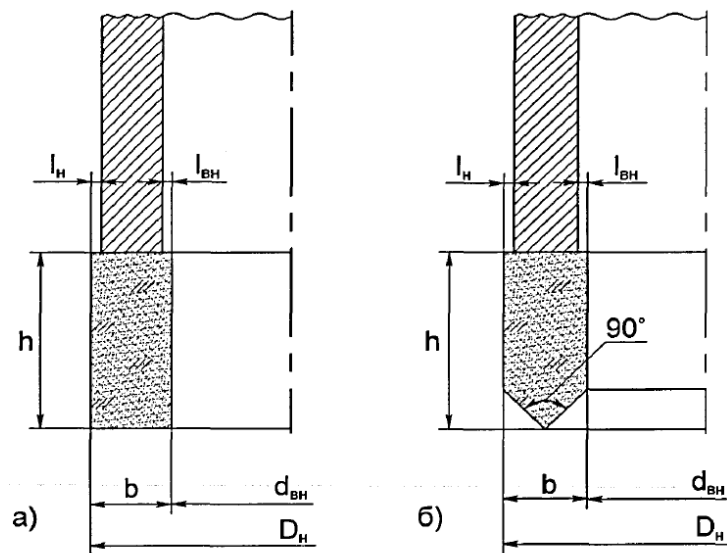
Геометрія алмазних кільцевих свердел [130]: а) пласка робоча торцева поверхня; б) загострена робоча торцева поверхня;
